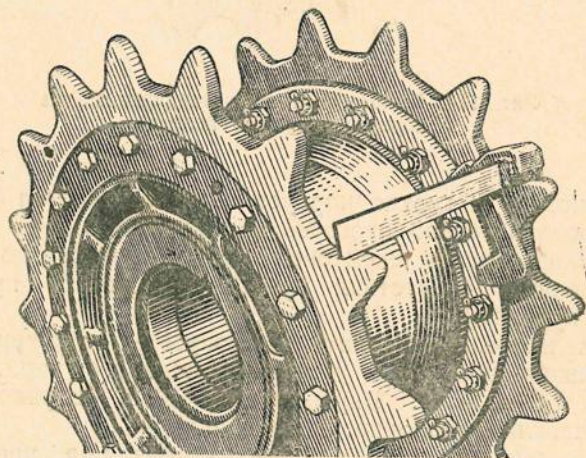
Проверка установки зубчатых венцов ведущего колеса при помощи приспособления
